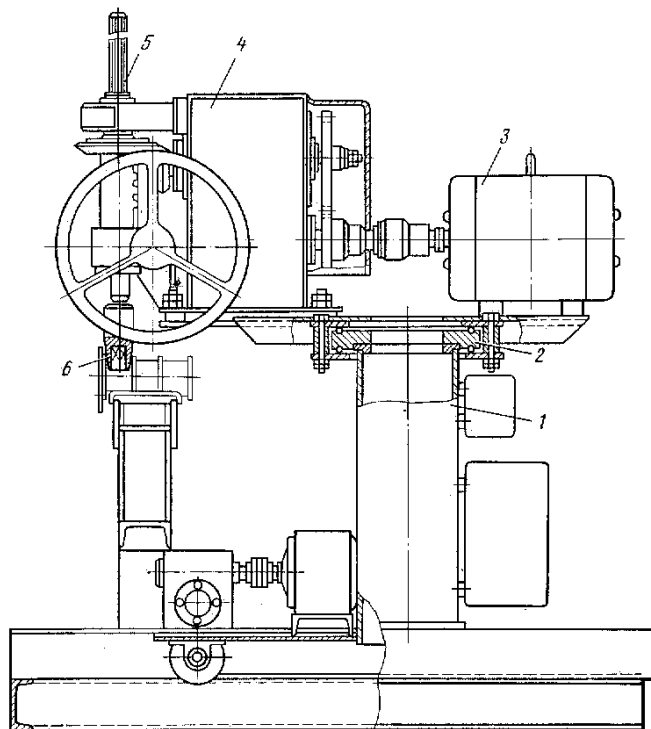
Електромеханічний стаціонарний гайковерт
